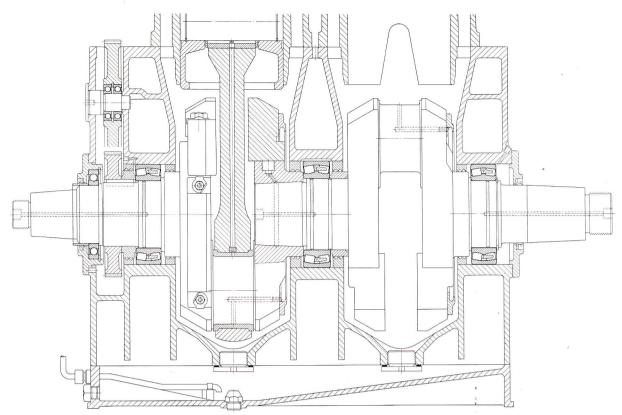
Corte de un motor diesel de dos cilindros con eje cigüeñal compuesto mediante aceite a presión. Fabricante: Hanseatische Motorenfabrik Penneberg, Hamburgo
